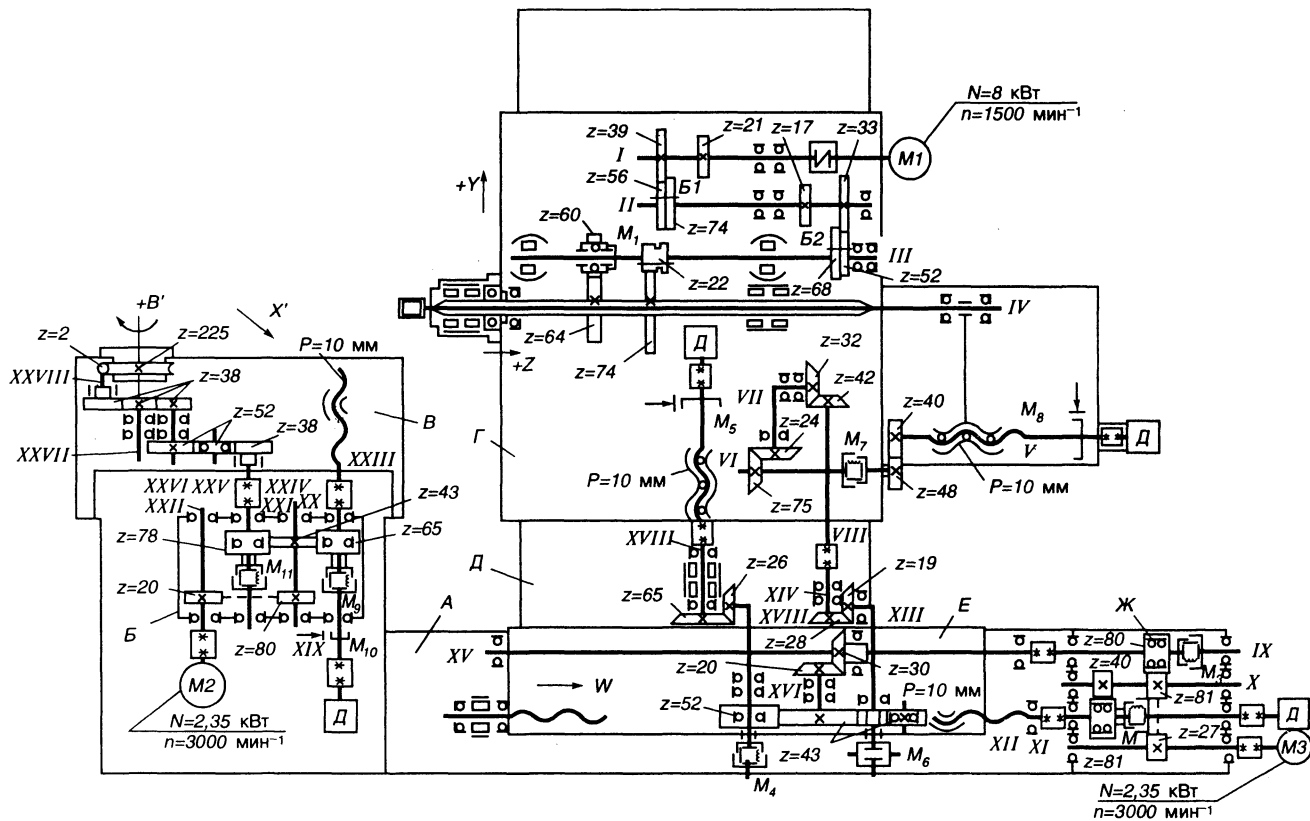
Кинематическая схема горизонтально-расточного станка с ЧПУ мод. 2611Ф2
